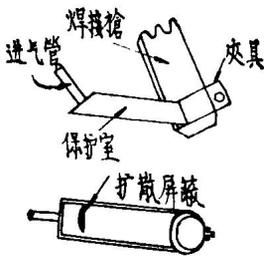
焊炬带有拖尾保护罩的保护装置
